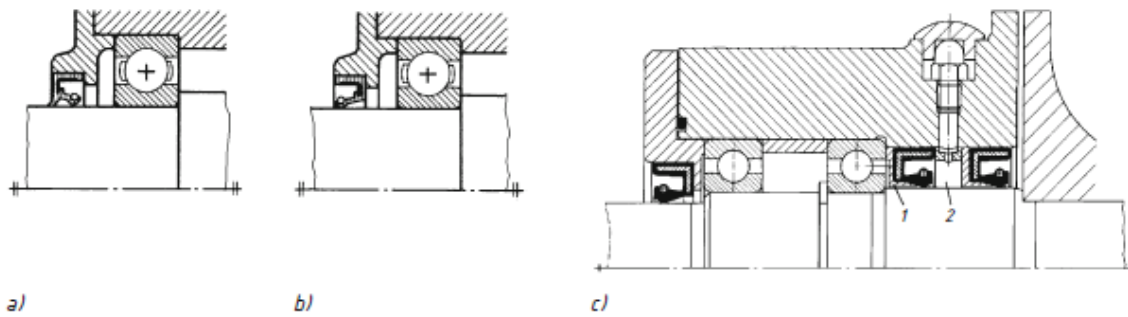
Einbaubeispiele für RWDR mit Abdichtung gegen: a) Schmiermittelaustritt, b) vorzugsweise Spritzwassereintritt, c) Wasser mit leichter Druckbeaufschlagung: 1 Stützring, 2 Fettfüllung
